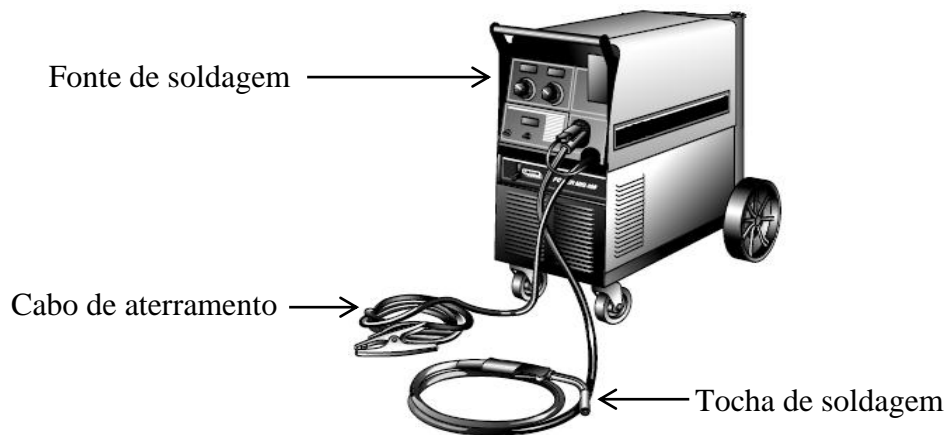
2: Fonte de soldagem. (Modificado Nadzam, 2011).
